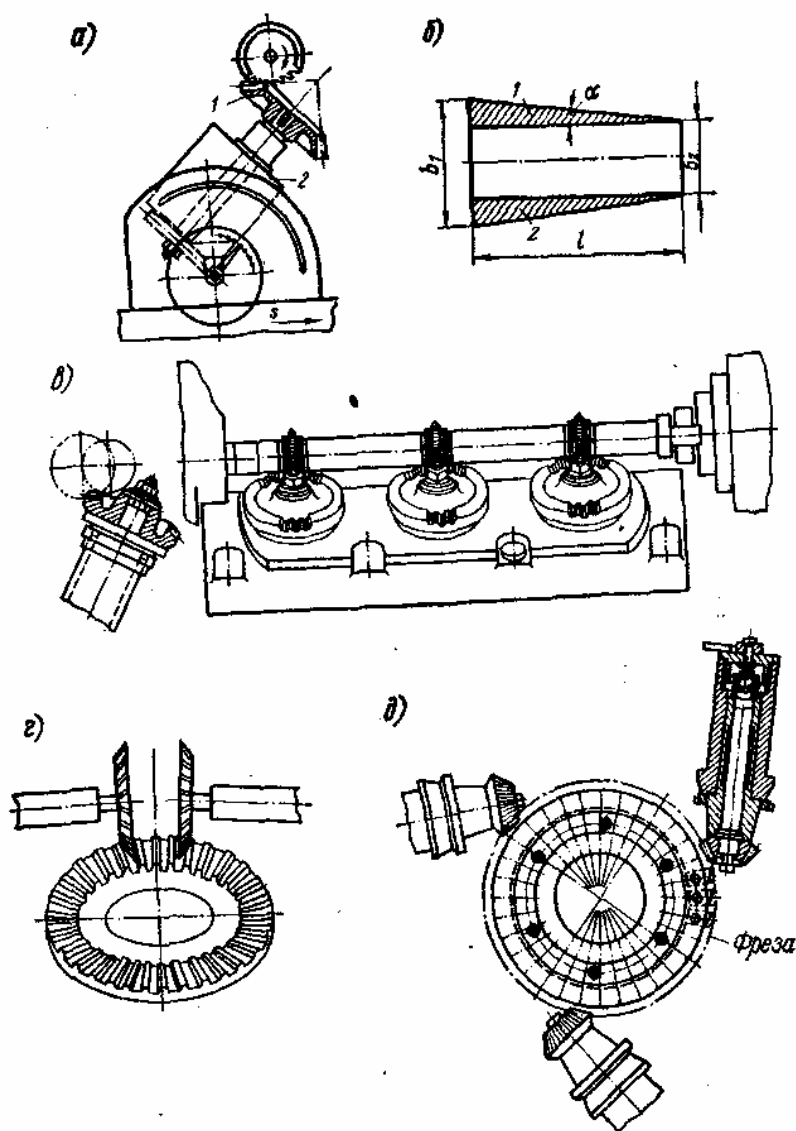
Зубофрезерование конического зубчатого колеса:
